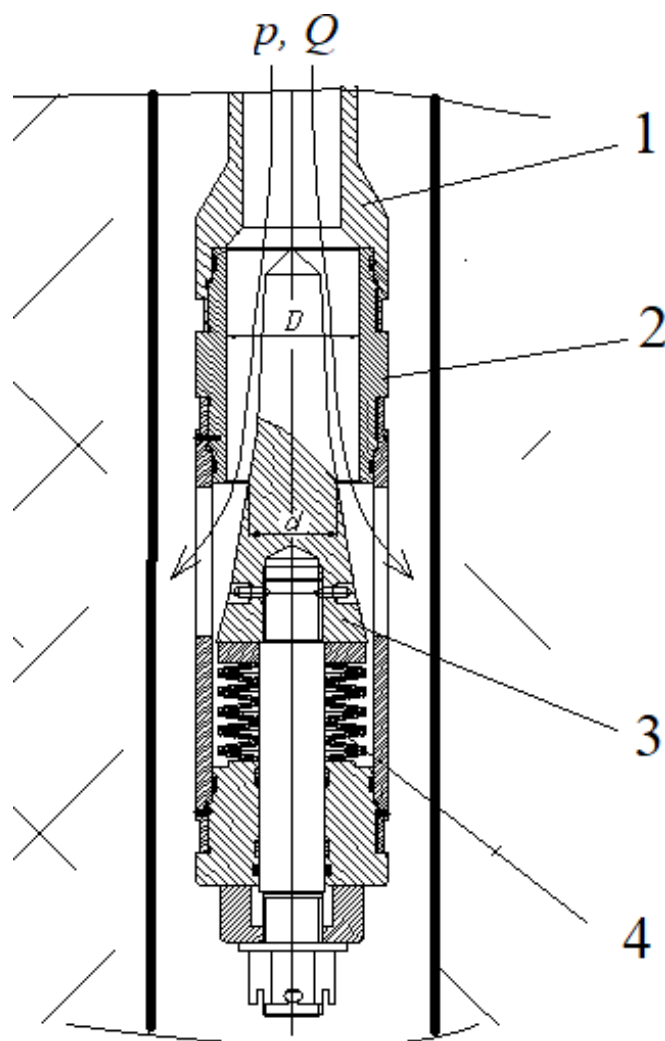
Конструктивна схема резонатора: 1 – перехідник, 2 – корпус, 3 – клапан (рухомий елемент), 4 – блок пружин
